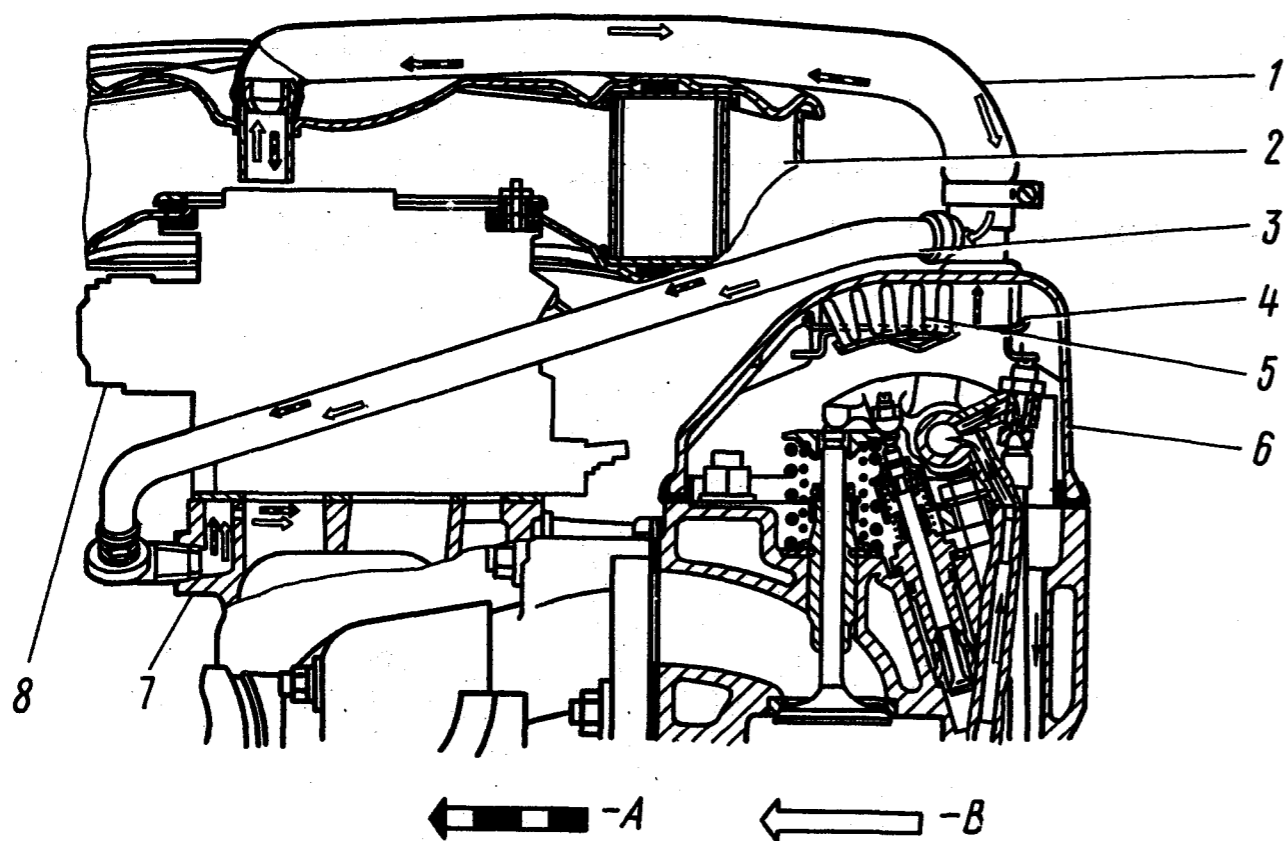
Схема вентиляции картера двигателя: А — картерные газы; В — чистый воздух; 1 и 3 — шланги; 2 — фильтр воздушный; 4 — маслоотражатель; 5 — элемент фильтрующий; 6 — крышка коромысел; 7 — труба впускная; 8 — карбюратор
